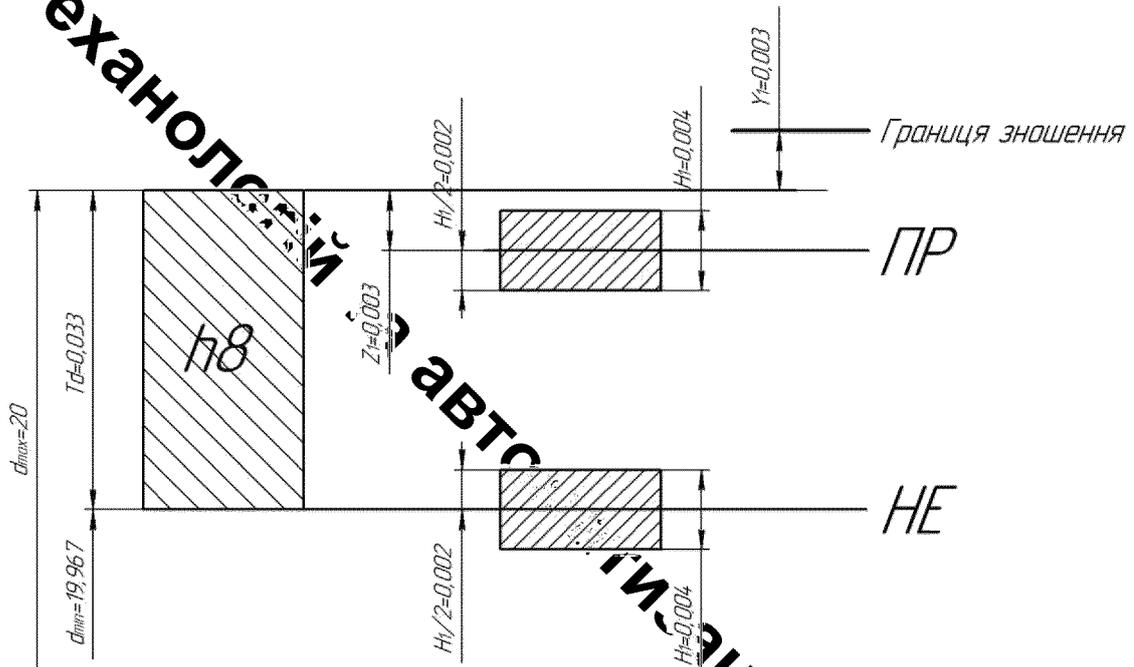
Схема розташування полів допусків для виготовлення калібр-скоби
